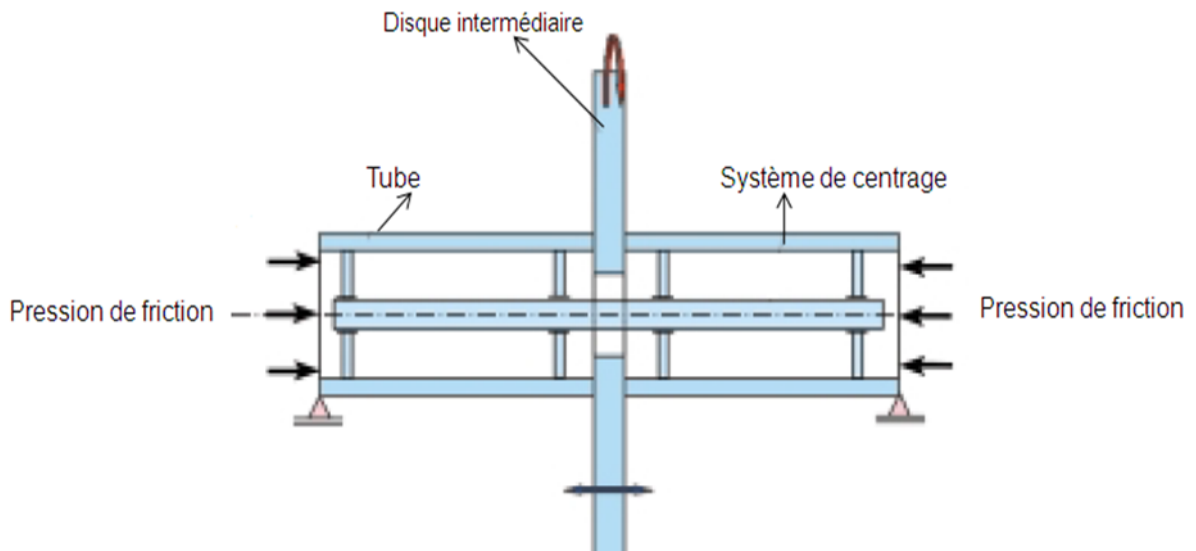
Schéma de principe d'une variante du procédé de soudage par friction
